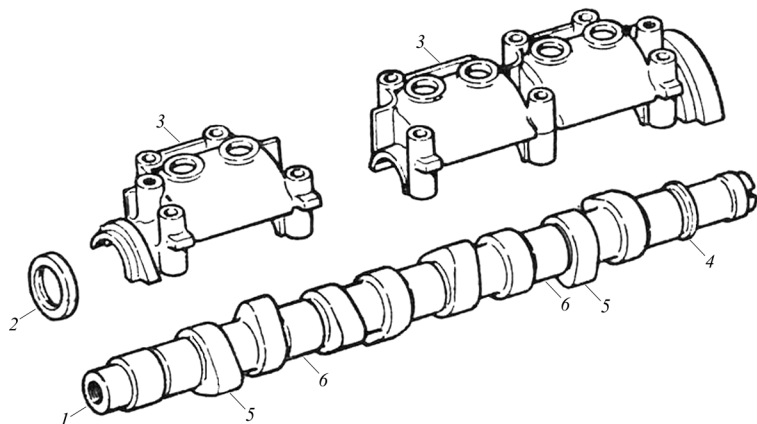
Распределительный вал и крышки подшипников распределительного вала: 1 – распределительный вал; 2 – сальник; 3 – крышка подшипников; 4 – эксцентрик привода топливного насоса; 5 – кулачки; 6 – опорные шейки
